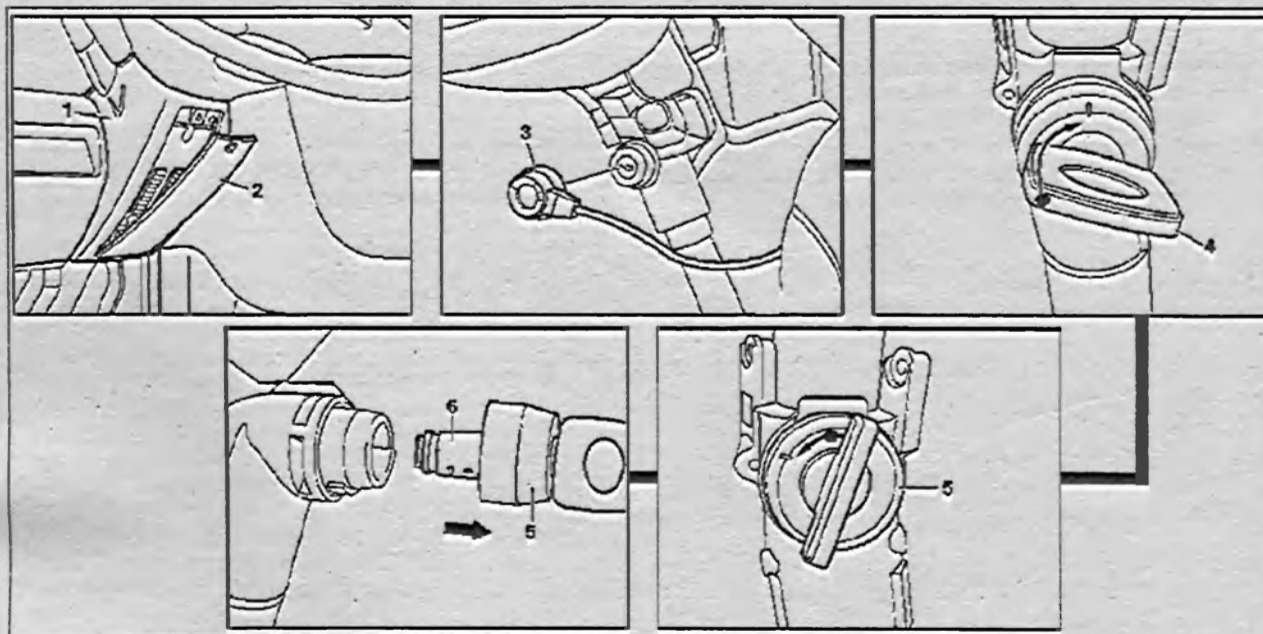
Блокировочный цилиндр замка блокировки рулевого вала:
